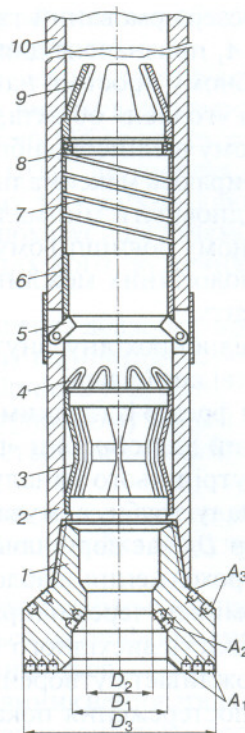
Схема механічного пристрою для вирізання аварійних ділянок бурових труб:
